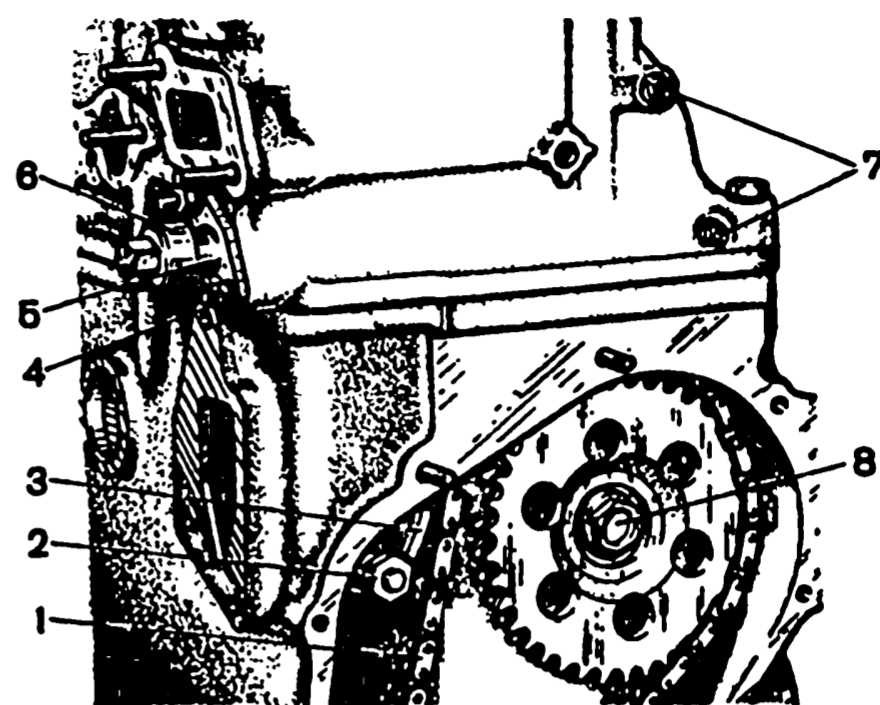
Снятие натяжителя и успокоителя цепи: 1 - цепь привода распределительного вала; 2 - болт крепления башмака; 3 - башмак натяжителя; 4 - гайка крепления натяжителя; 5 - корпус натяжителя; 6 - колпачковая гайка натяжителя; 7 - болты крепления успокоителя цепи; 8 - болт крепления звездочки валика привода масляного насоса
